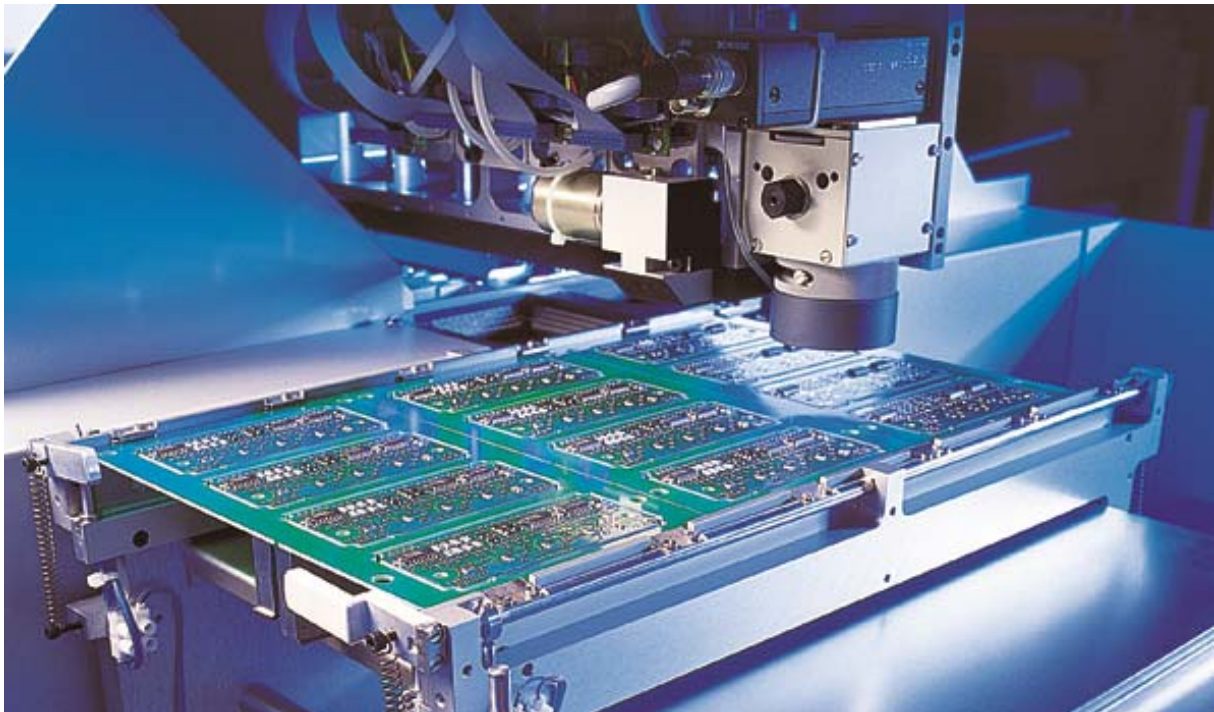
Präzise Bestückung durch die magnetische Messtechnik
